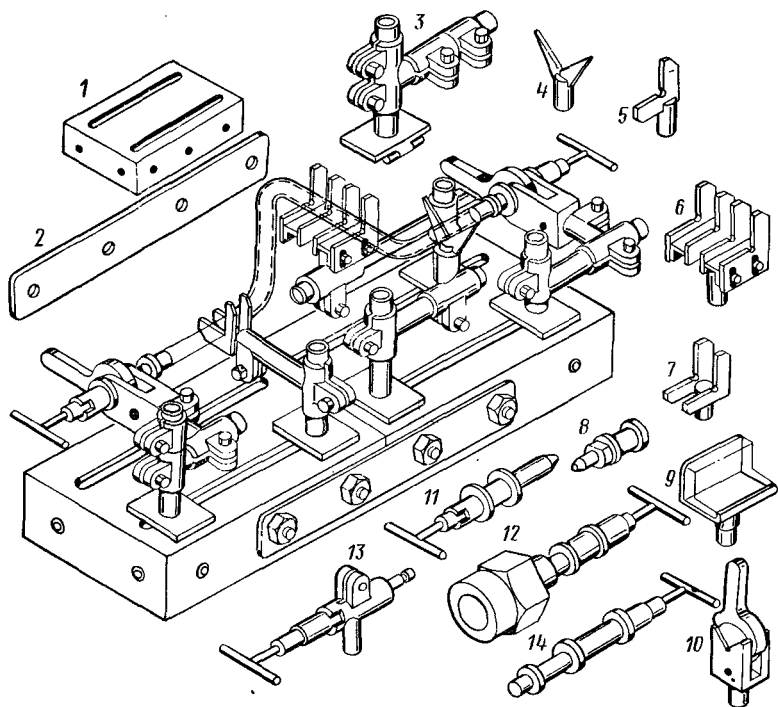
Универсально-сборное приспособление для изготовления и контроля деталей из труб по первой группе точности
